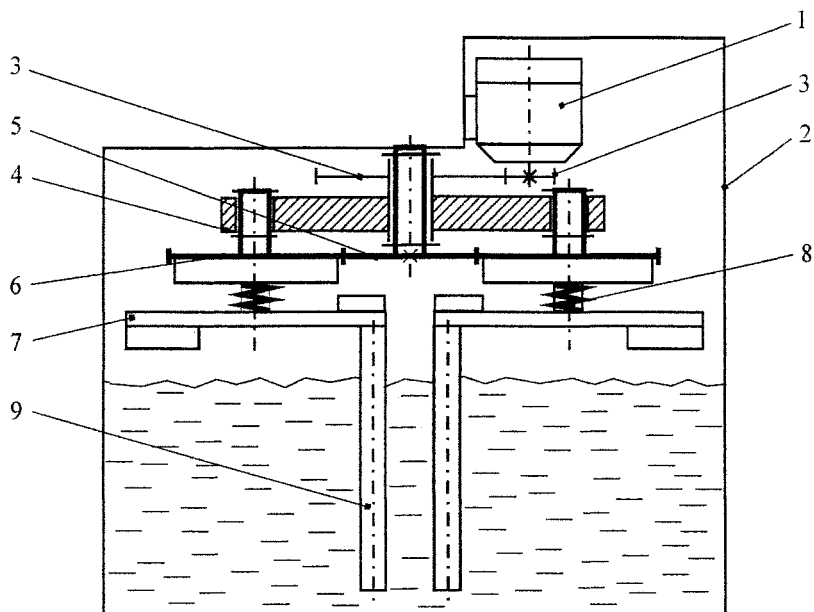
Схема планетарного привода смесителя с упругим элементом на сателлите: 1 – двигатель; 2 – корпус; 3 – передаточный механизм; 4 – водило; 5 – центральная шестерня; 6 – сателлит; 7 – баланс; 8 – упругий элемент; 9 – рабочий орган
